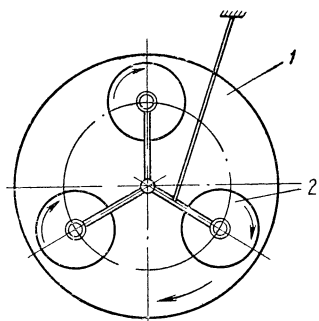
Схема станка для односторонней шлифовки с вращающимся шлифовальником и тремя головками. 1 — шлифовальник; 2 — головка с деталями.
